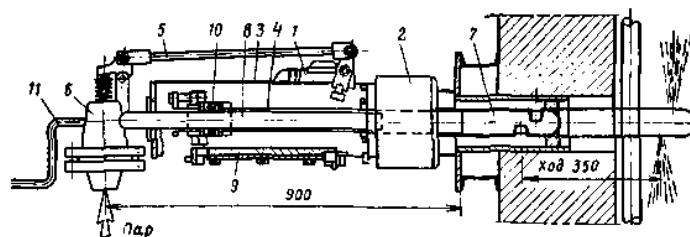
Аппарат для паровой обдувки экранов: 1 – электродвигатель; 2 – редуктор; 3 – корпус; 4 – шпиндель; 5 – рычажной механизм; 6 – клапан; 7 – сопловая головка с двумя соплами; 8 – центральная неподвижная труба; 9 – направляющая; 10 - сальник; 11 – рукоятка.
